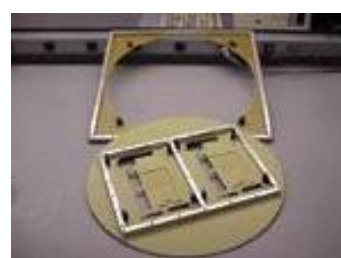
Cadru la trecerea prin val Fig. 2.3.8. Structura cadrului de lipire Fig. 2.3.9. Cadru multifuncțional
